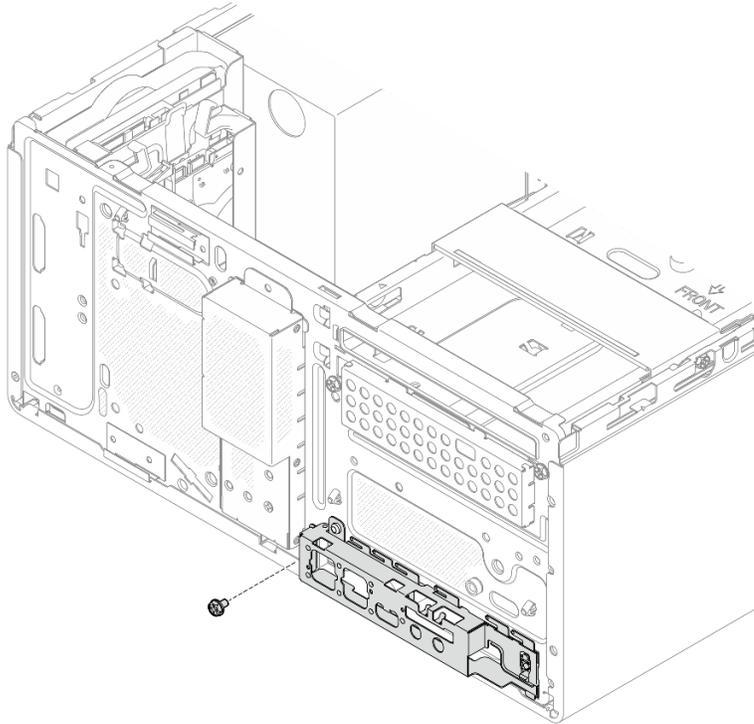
Removendo o parafuso que fixa o suporte de E/S frontal
